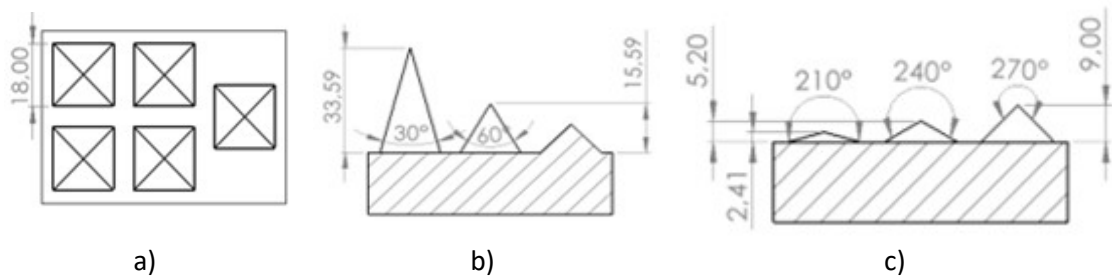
Geometría de las pirámides (a) Planta (b) Perfil frontal (c) Perfil posterior.
